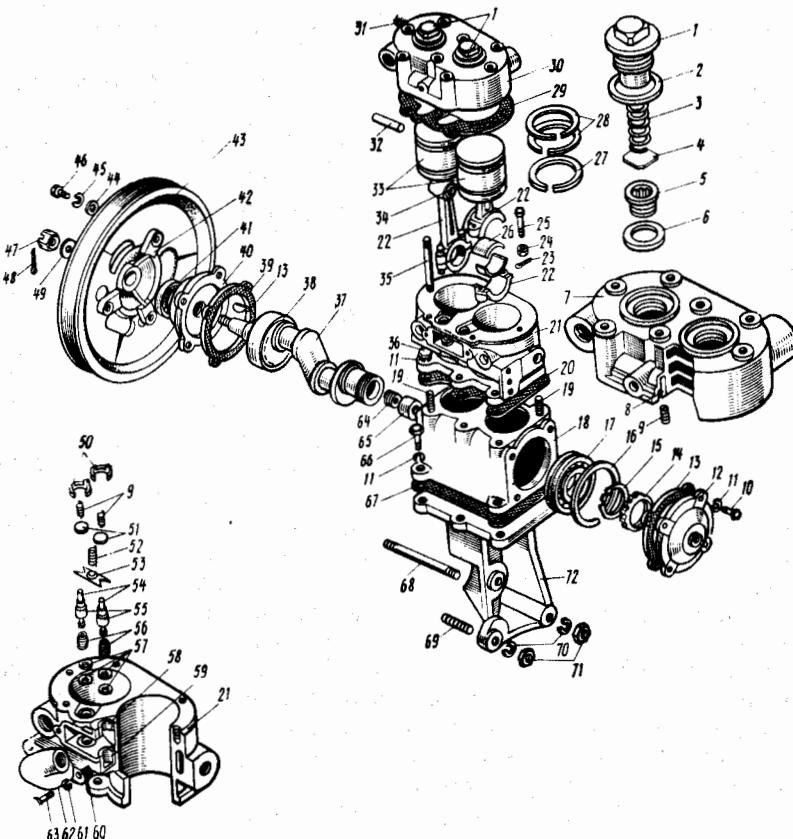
Детали компрессора автомобиля ЗИЛ-431410:
